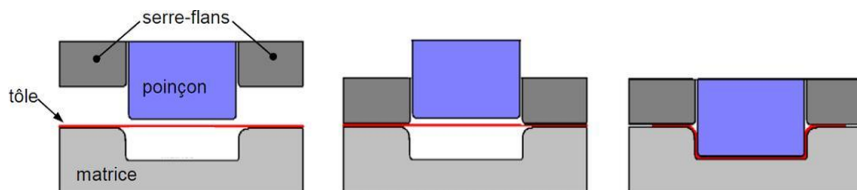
Principe d'emboutissage (pièces forgées) .
